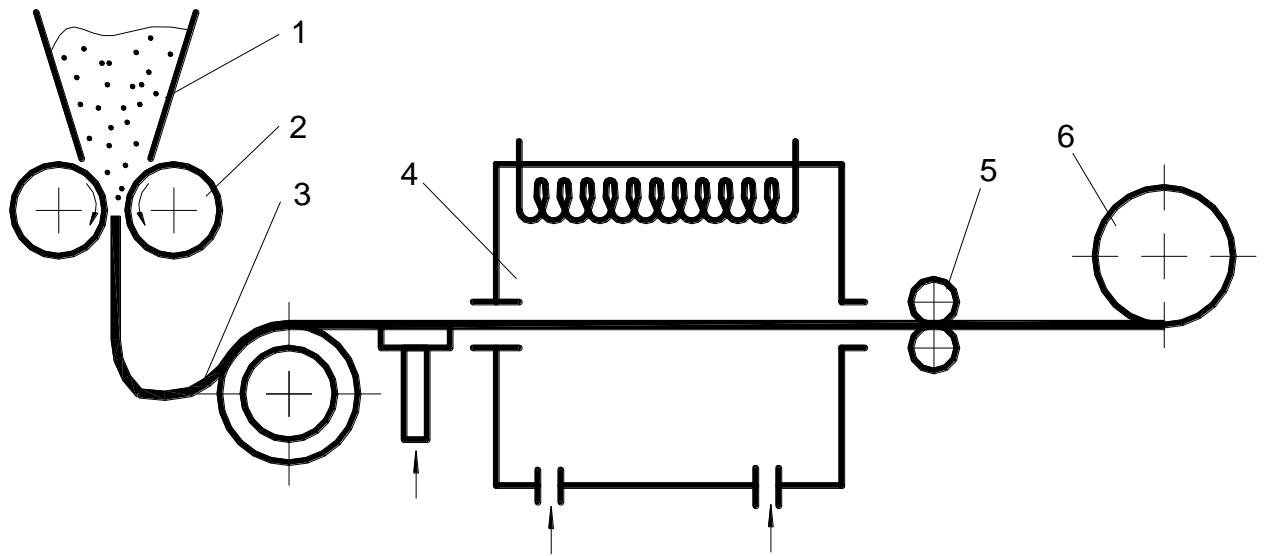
Технология изготовления непрерывной полосы из металлических порошков
